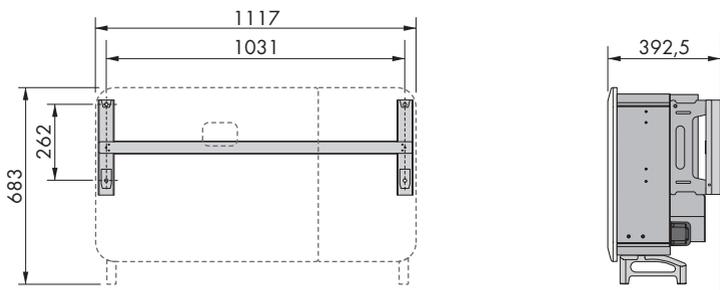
Dimensioni del supporto di montaggio (indicazioni in mm)
